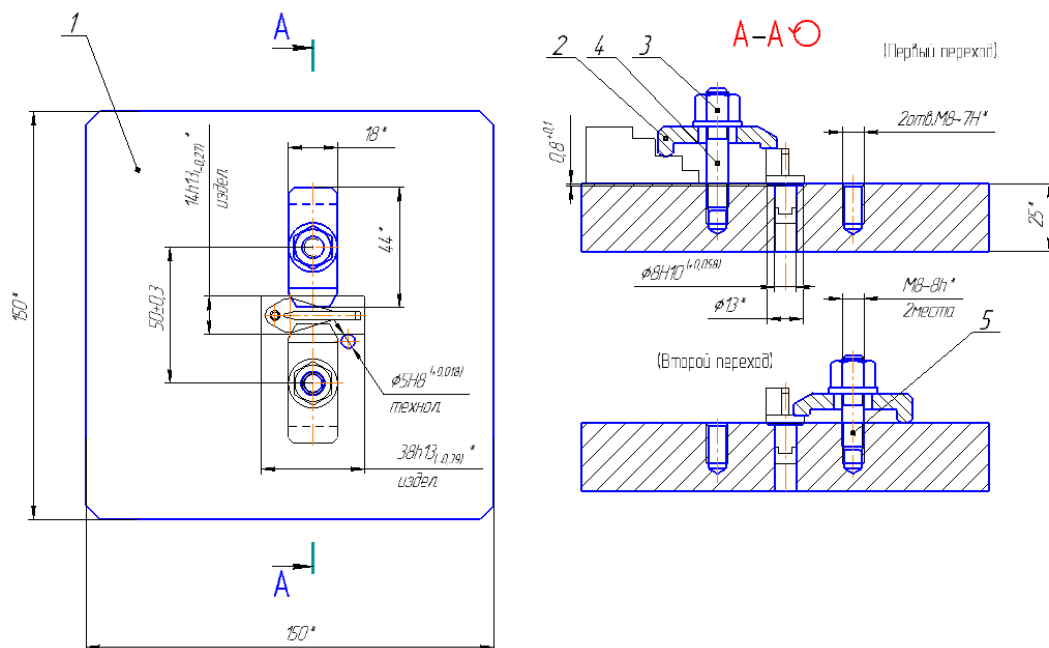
Приспособление для фрезерной обработки ребра  $3h14$ : 1 – опорная плита, 2 – прихват, 3 – гайка, 4, 5 – шпилька.
